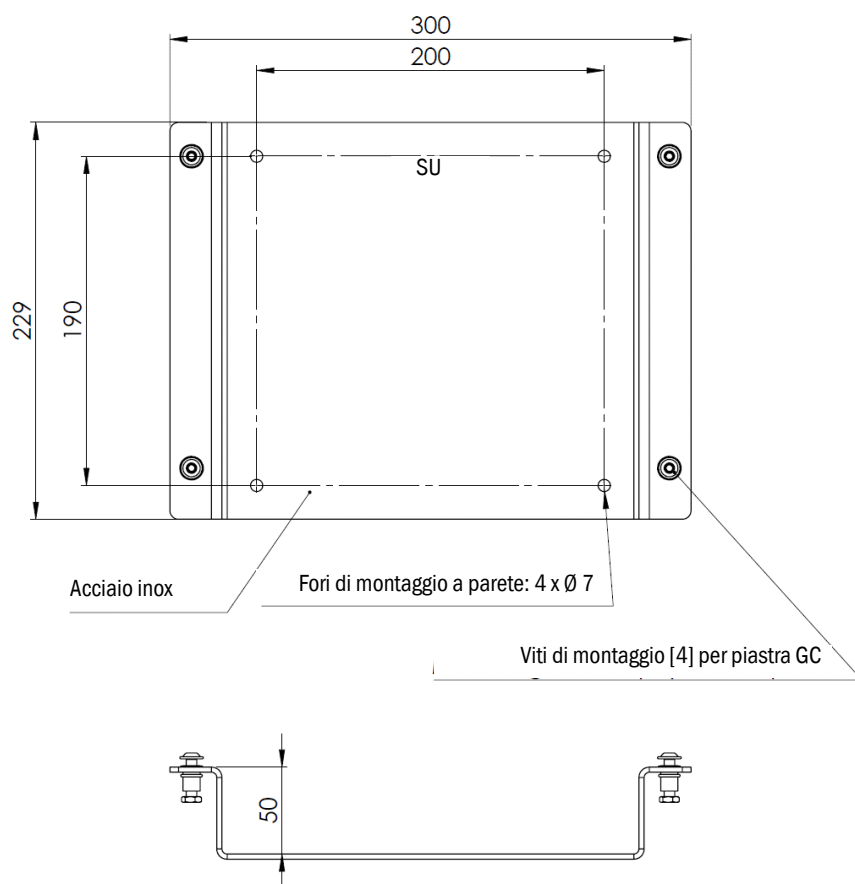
Piastra per montaggio a parete opzionale (dimensioni e montaggio)
